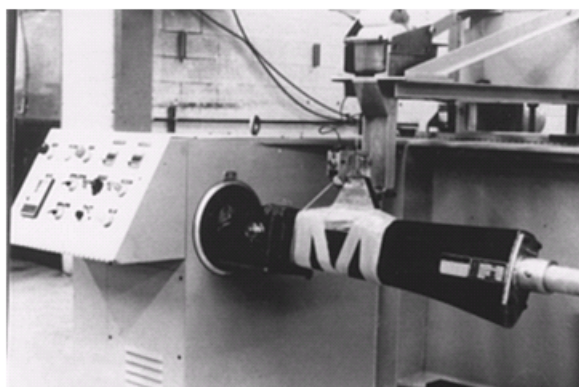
Configurazione complessa di winding per il V22 grip assembly
